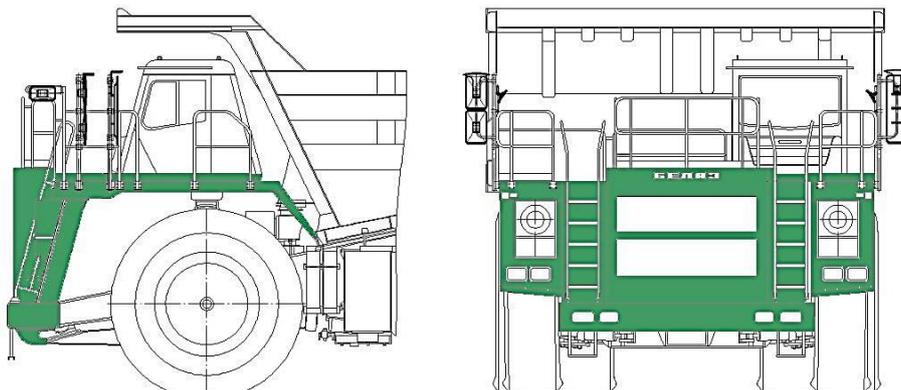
Общий вид палубы карьерного самосвала БелАЗ-75131
